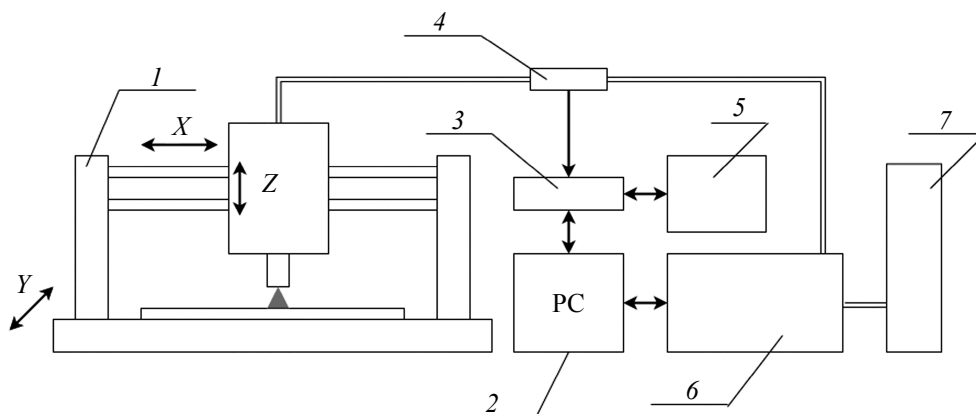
Экспериментальный стенд по 3D-наплавке на базе станка с ЧПУ: 1 – 3-координатный станок с ЧПУ портального типа; 2 – ПК; 3 – АЦП/ЦАП; 4 – датчики силы тока и напряжения; 5 – система ЧПУ; 6 – сварочный полуавтомат; 7 – баллоны с защитным газом
